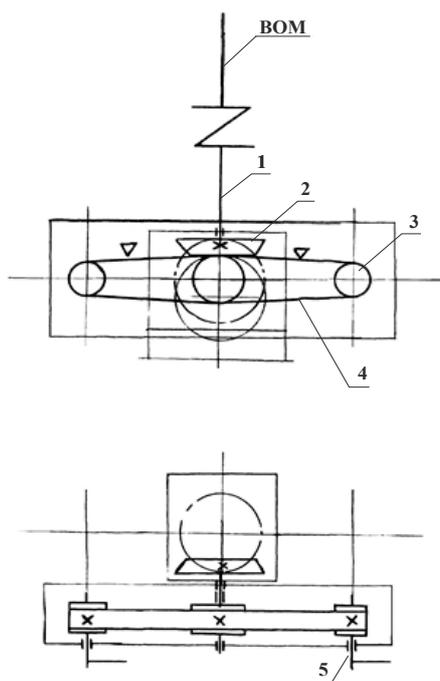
Кинематическая схема установки: ВОМ — вал отбора мощности; 1 — карданный вал; 2 — конический редуктор; 3 — шкив; 4 — клиноременная передача; 5 — ножевой узел
